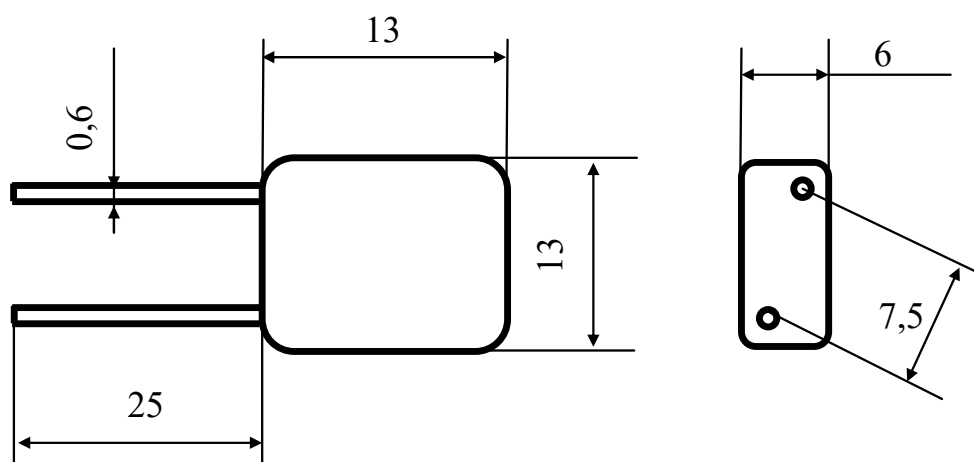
Внешний вид конденсатора КМ-4 (типоразмер 4)
